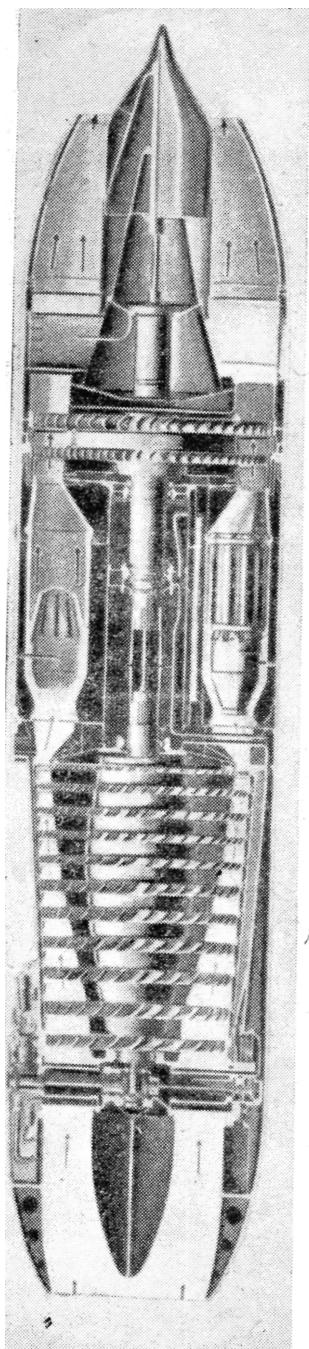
Турбореактивный двигатель с осевым компрессором.
